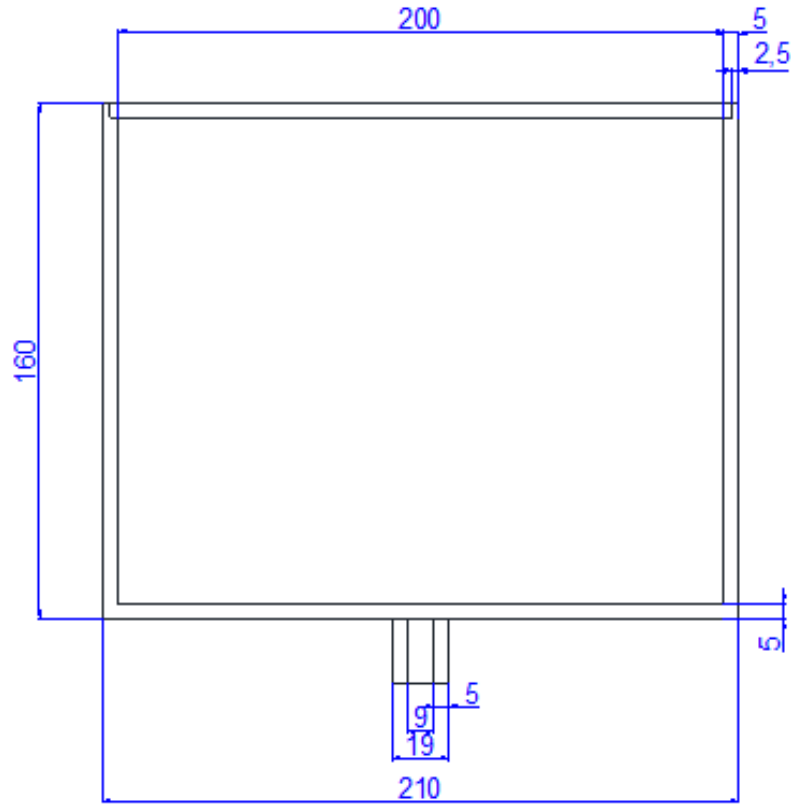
Tanque de almacenamiento (dimensiones en mm).
